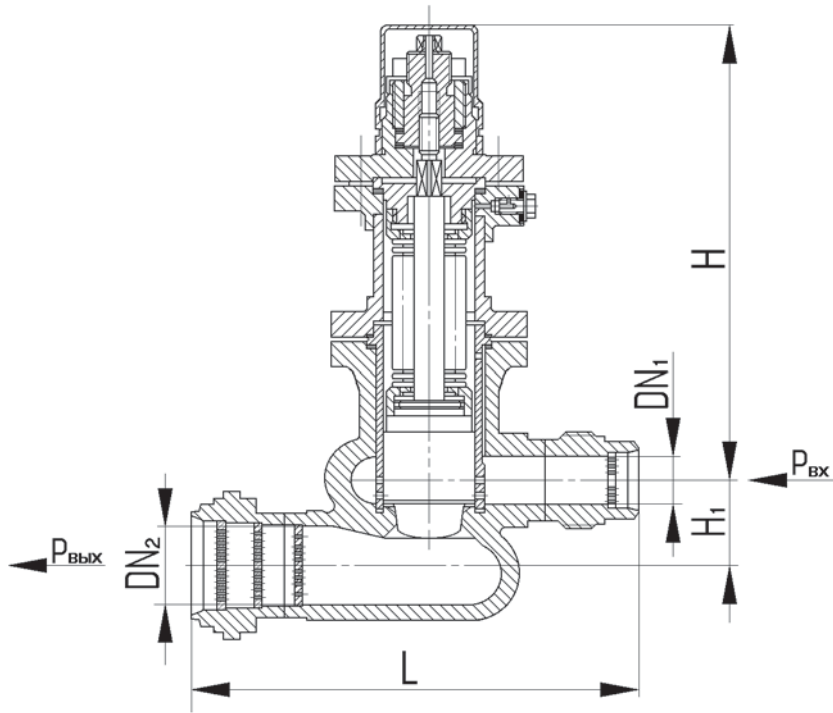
Клапан дроссельный проходной с патрубками под приварку
